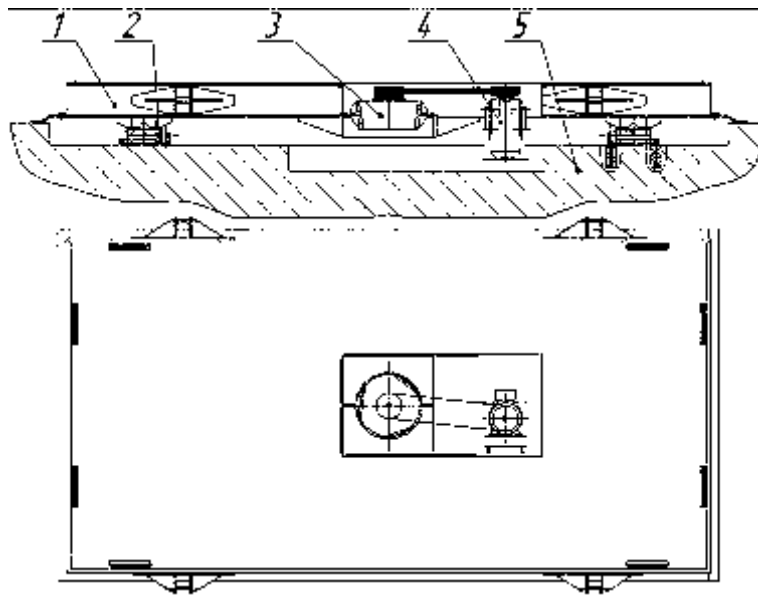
Віброплощадка для формування плит залізобетонних лотків із розмірами рухомої рами у плані 6,3×3,2 м: 1 – рухома рама; 2 – пружна опора; 3 – вібробуджувач крутильних коливань; 4 – електродвигун; 5 – фундамент
